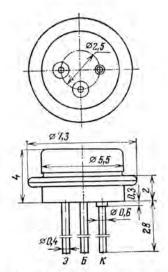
Габаритный чертеж транвисторов КТ306 и КТ316.
